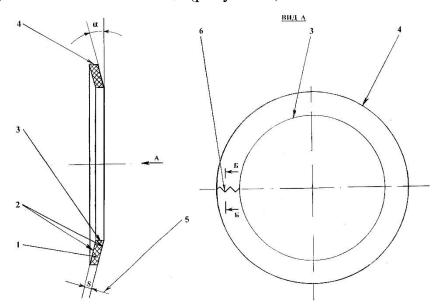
Уплотнительное кольцо: 1 —уплотнительное кольцо; 2торцевая поверхность; 3,4 — внутренняя и внешняя цилиндрическая поверхность; 5 — толщина кольца; 6 — зубчатые разрезы
